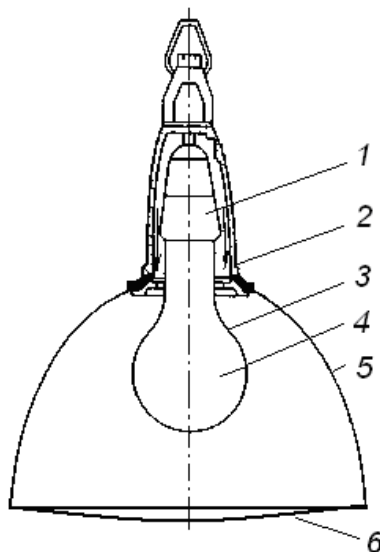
Схема зеркального светильника с защитным стеклом:
